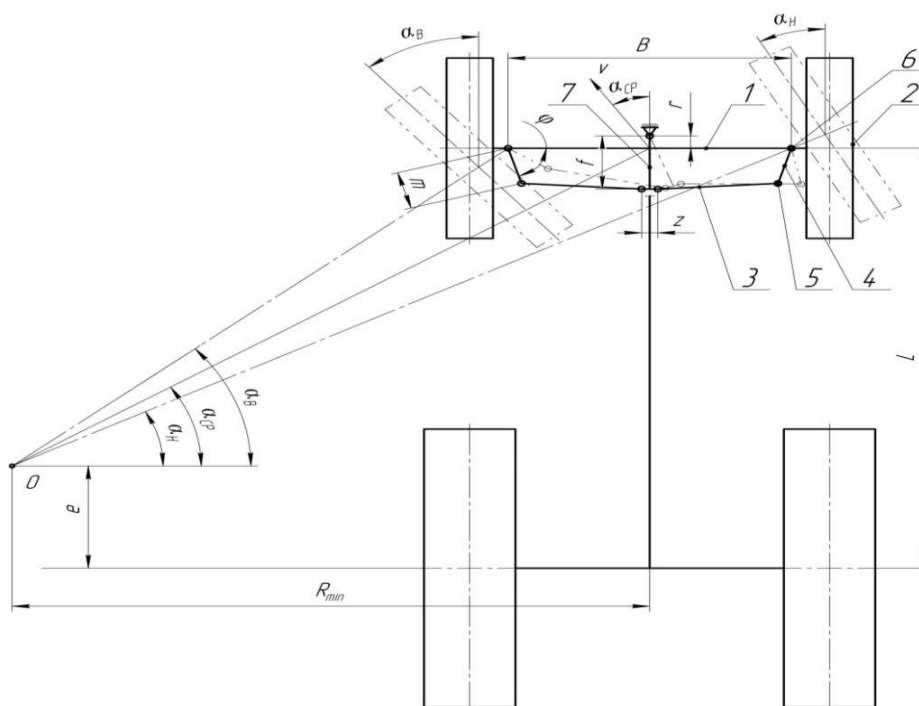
Кинематическая схема фактического поворота колесной машины, реализуемого разрезной рулевой трапецией: 1 – передний мост; 2 – управляемые колеса; 3 – поперечные тяги; 4 – боковые рычаги; 5 – сферические шарниры; 6 – шкворни; 7 – рулевая сошка
